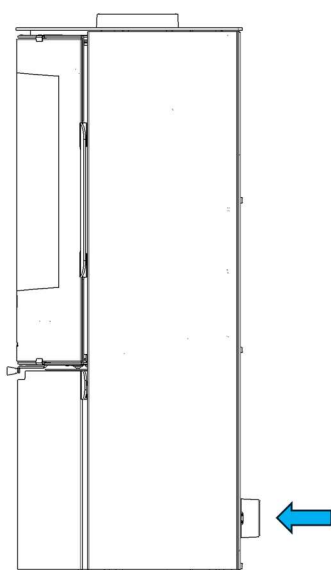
OPZIONE 2 Presa d'aria esterna, utilizzando i set di collegamento
